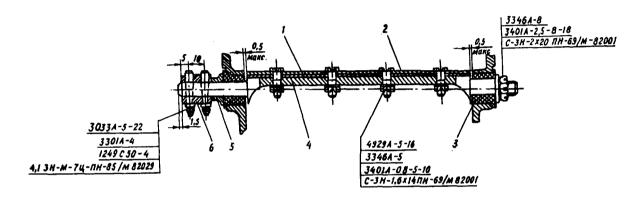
Установка заслонки подогрева во всасывающем патрубке карбюратора: 1— усиливающая накладка; 2— заслонка Ш6803-18; 3— резиновая втулка Ш6803-51; 4— ось Ш6803-53; 5— втулка Ш6803-52 (Д16АТ); 6— поводок А6803-50
